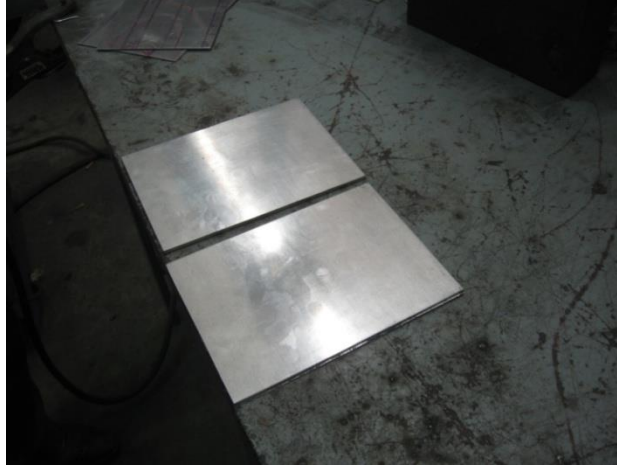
Plaque d'aluminium 7075 T6 prête pour le soudage (épaisseur = 2,5 mm)
